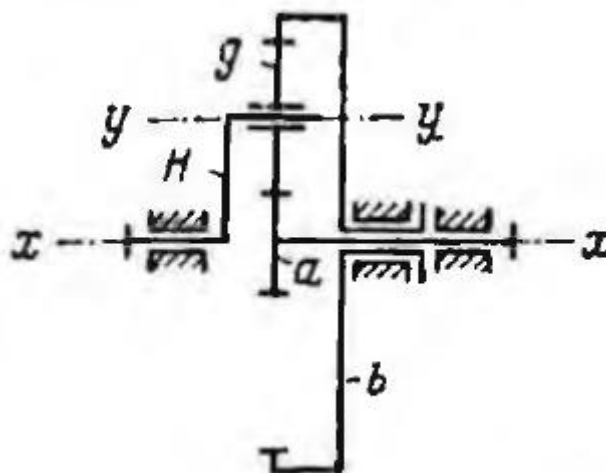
Схема планетарного механізму [8, 9, 11]
